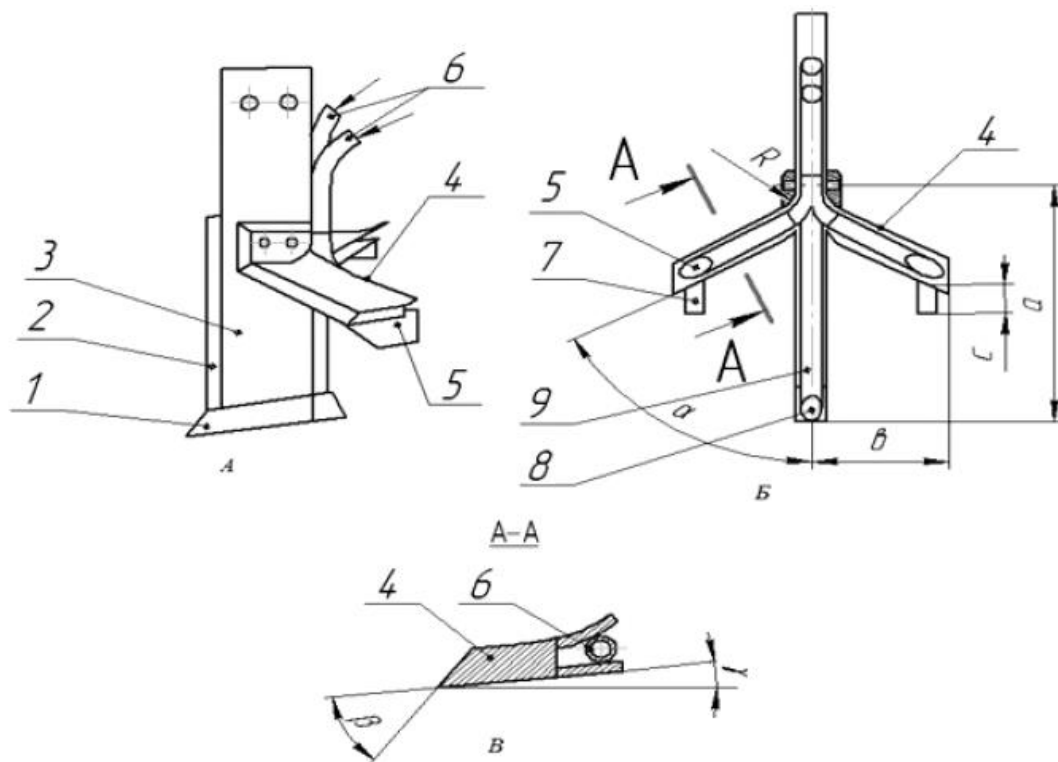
Схема робочого органу для внесення добрив: 1 – долото; 2 – розсіювач; 3 – стовба; 4 – ніж; 5 – горизонтальний щілювач; 6, 9 – трубчатий удобрювач; 7 – наконечник-живильник; 8 – вертикальний щілювач.
